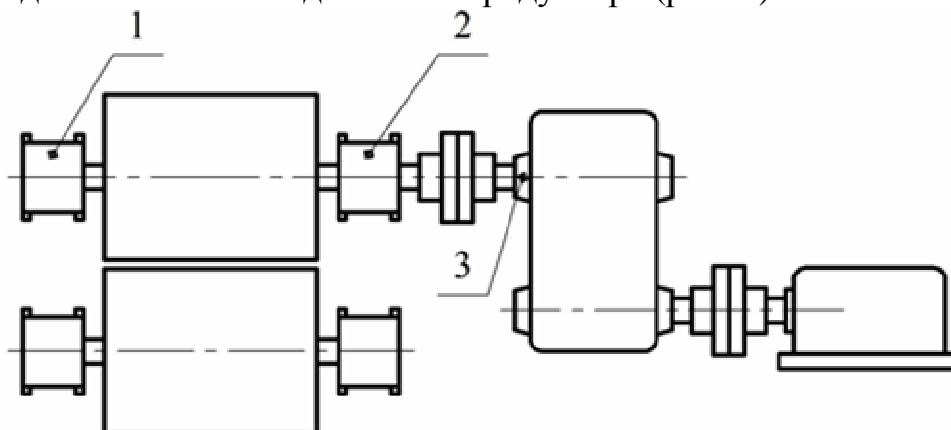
Схема установки измерительных датчиков: 1 – подшипниковая опора валка с холостой стороны; 2 – подшипниковая опора валка с приводной стороны; 3 – бобышка тихоходного вала редуктора
